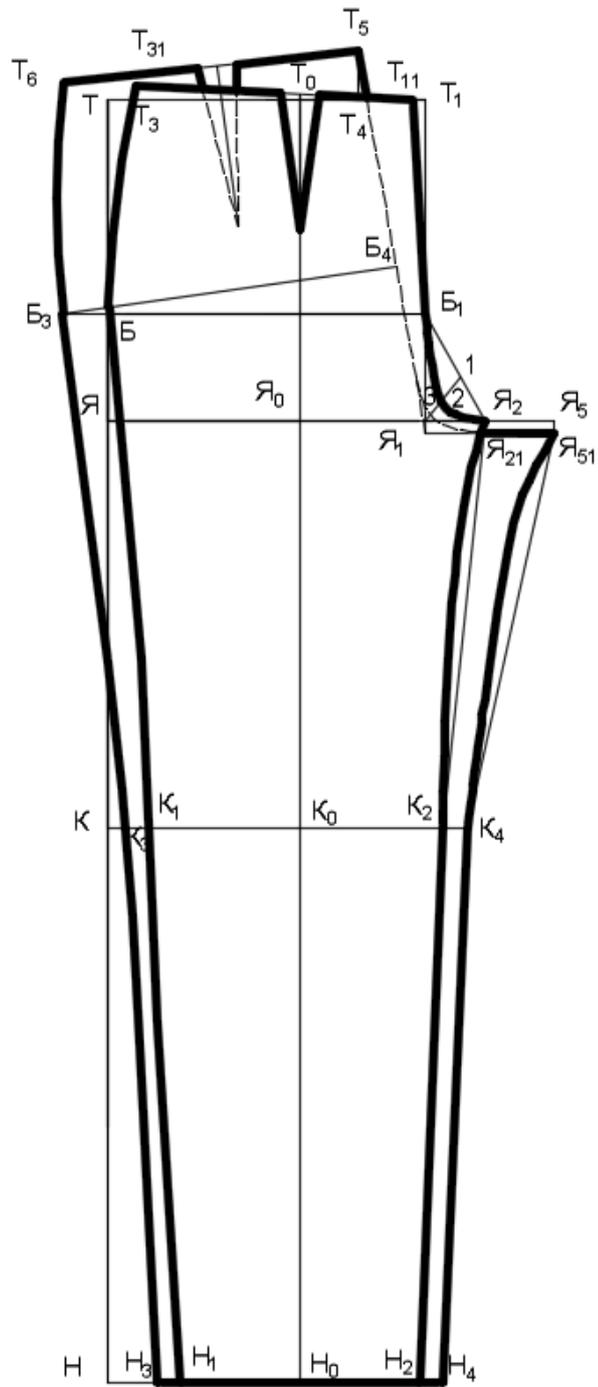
Схема построения чертежа конструкции женских брюк
